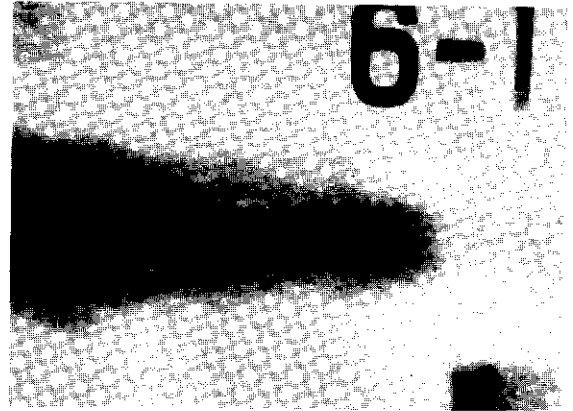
Fusión incompleta en la interfase de la soldadura.
